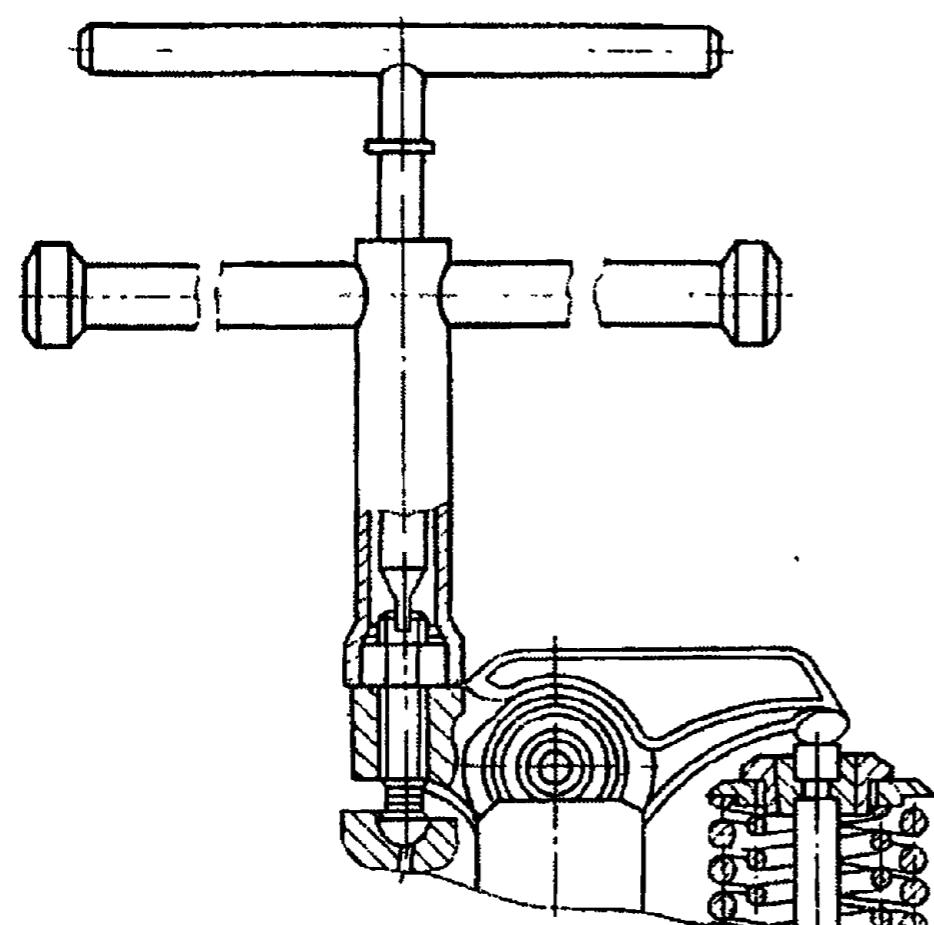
Приспособление И801.14.000 для регулирования клапанов двигателя
